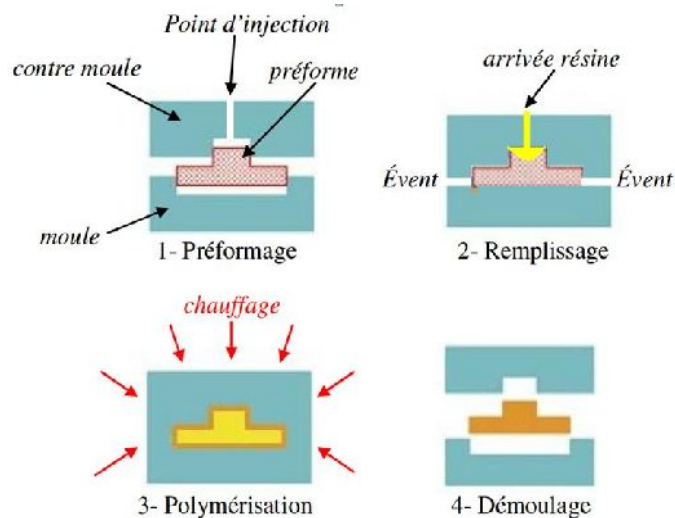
Procédés d'injection RTM (Resin Transfert Moulding) [2]
